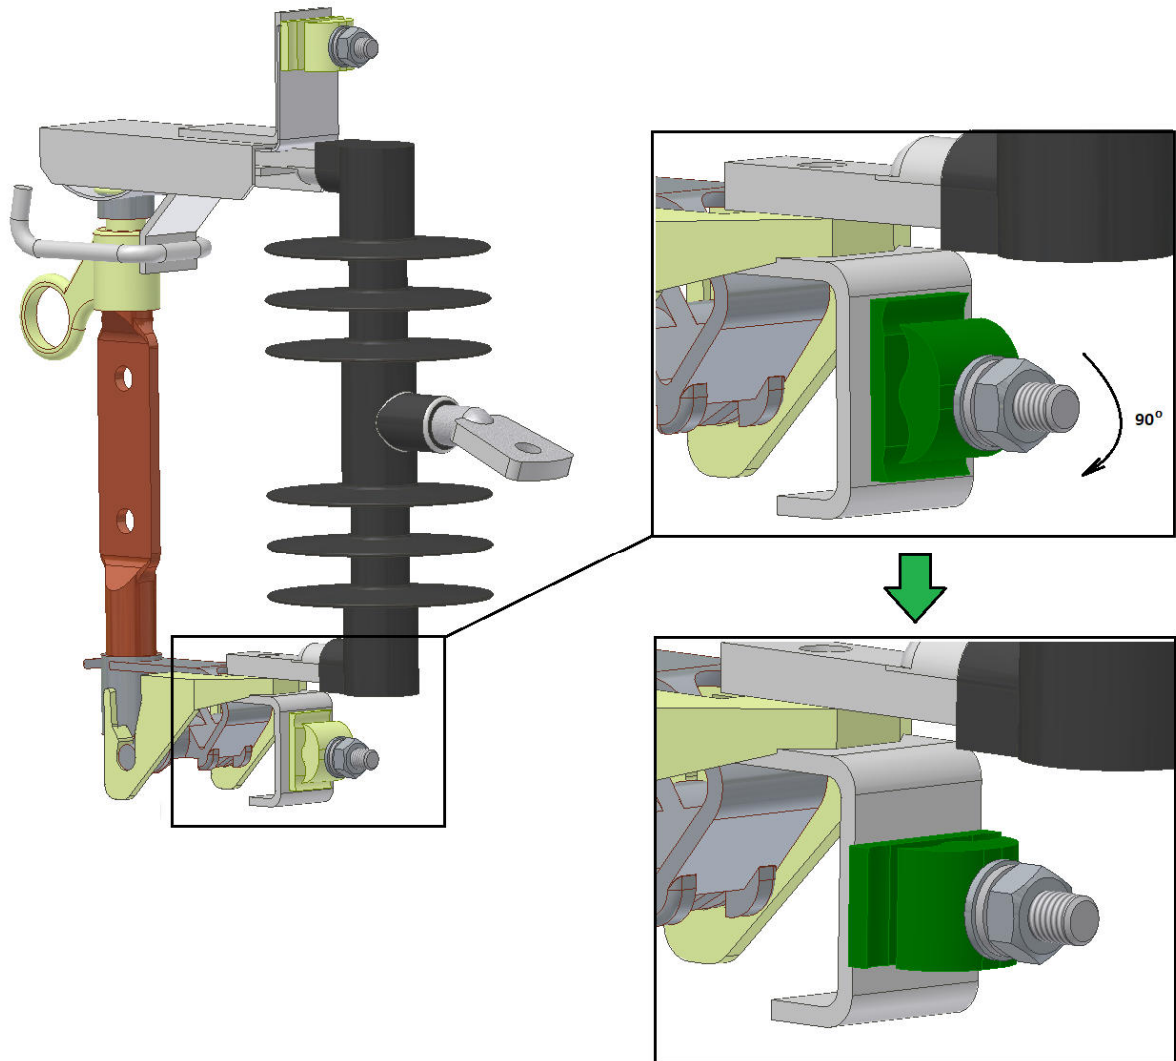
Разворот нижнего терминала Cut-Out 315 А
